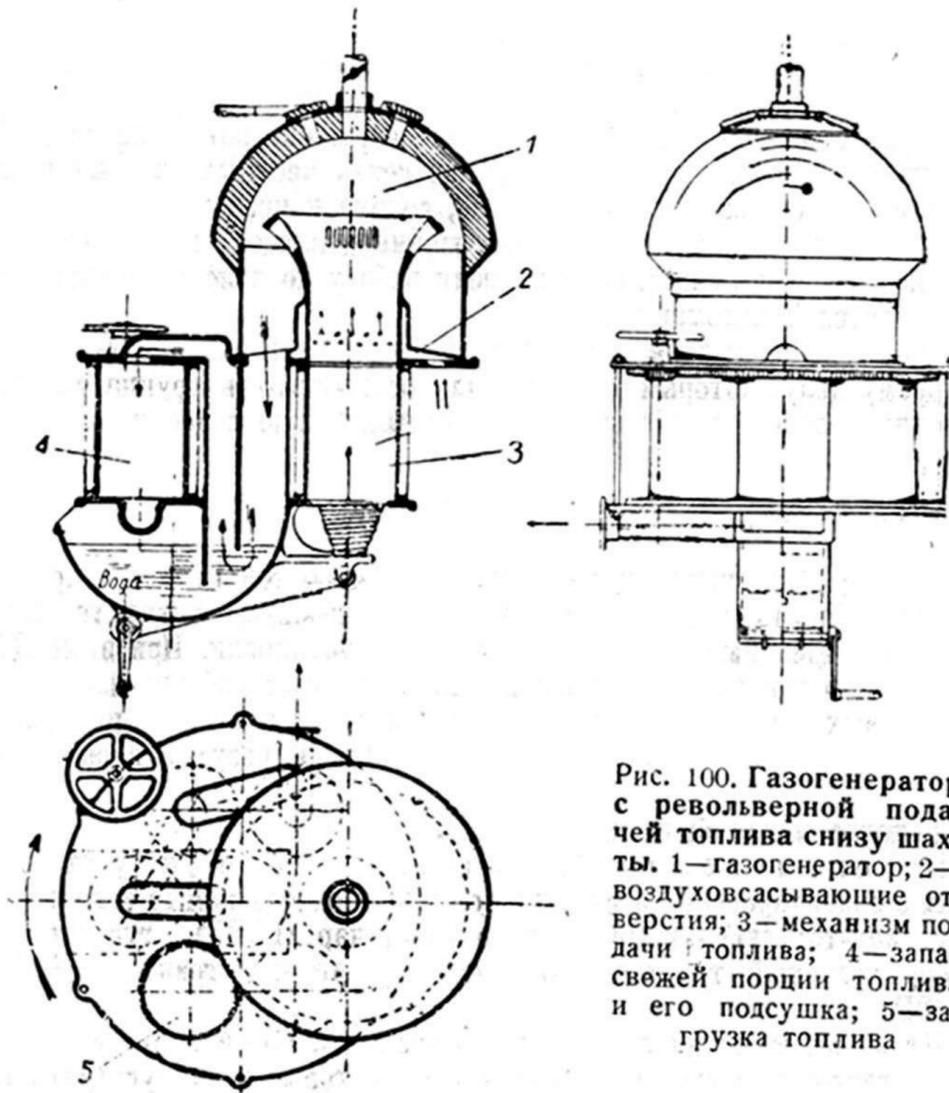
Газогенератор с револьверной подачей топлива снизу шахты. 1—газогенератор; 2—воздуховсасывающие отверстия; 3—механизм подачи топлива; 4—запас свежей порции топлива и его подсушка; 5—загрузка топлива
